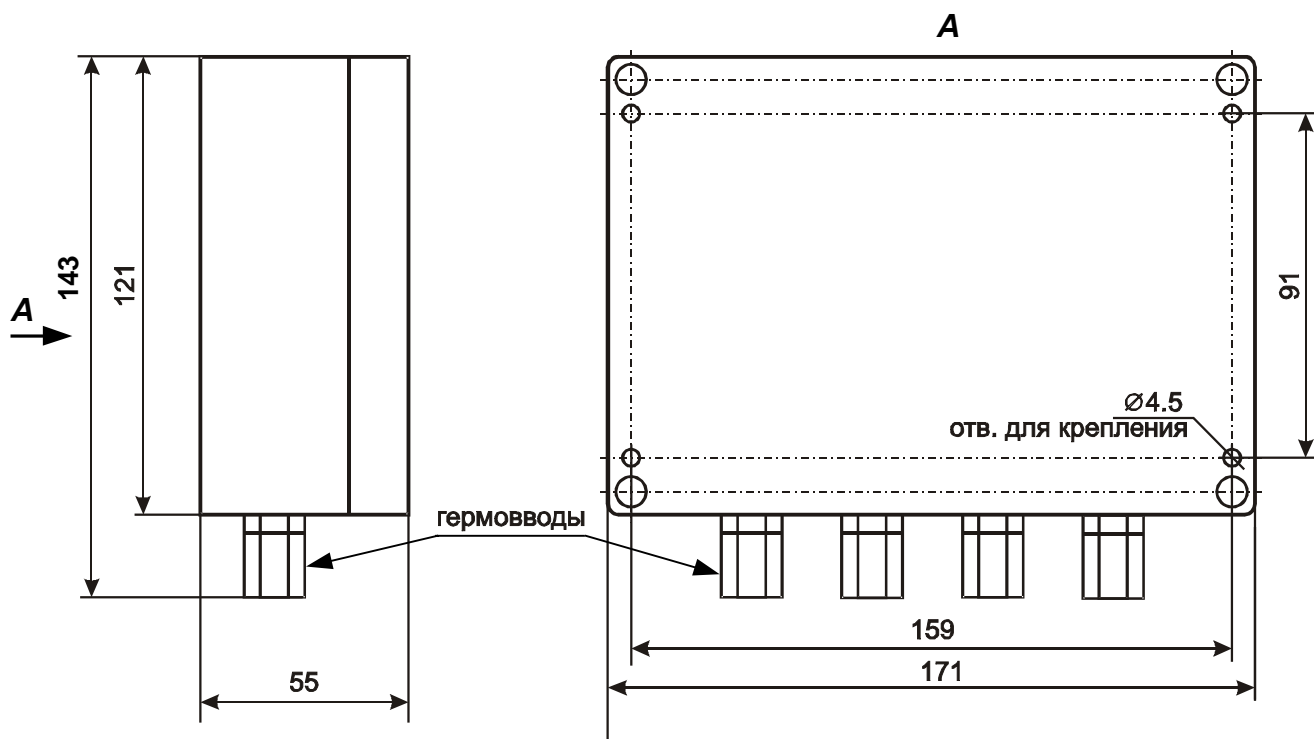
Внешний вид и габаритные размеры БРЛ в исп. IP65
